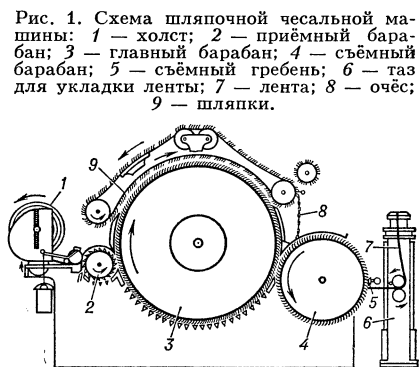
Схема шляпочной чесальной машины: 1 — холст; 2 — приёмный барабан; 3 — главный барабан; 4 — съёмный барабан; 5 — съёмный гребень; 6 — таз для укладки ленты; 7 — лента; 8 — очёс; 9 — шляпки.
